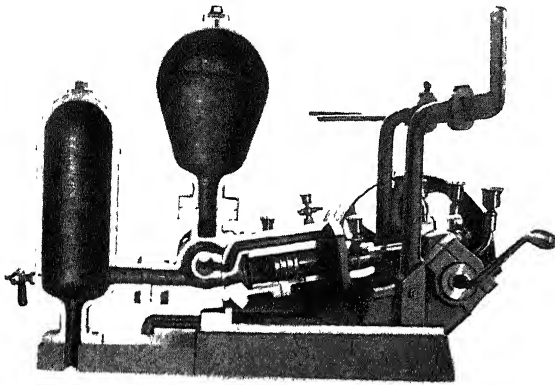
Wassersäulenmaschine von KROBER mit schwingendem Zylinder. (Deutsches Museum.)
